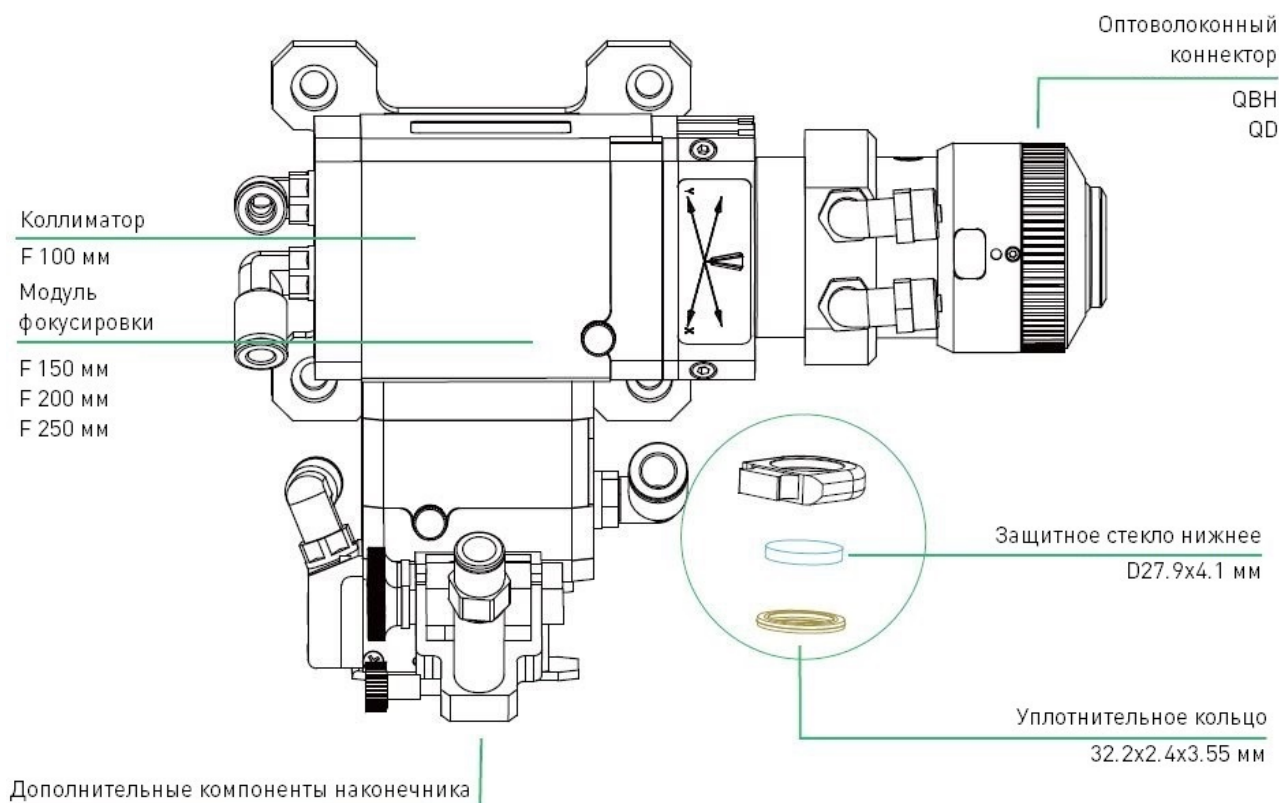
Схематическое изображение лазерной сварочной головки AK090.
